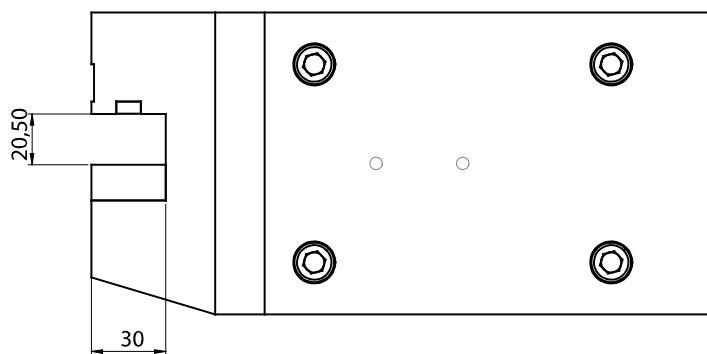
Чертеж канала для вставки пуансона. Вид головки обжатия сверху
